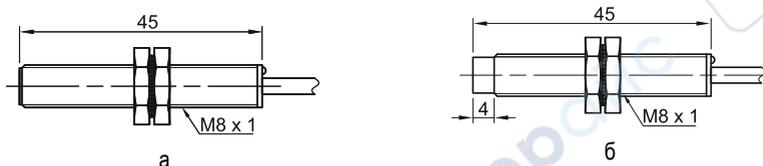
Габаритные и установочные размеры датчиков LA08
